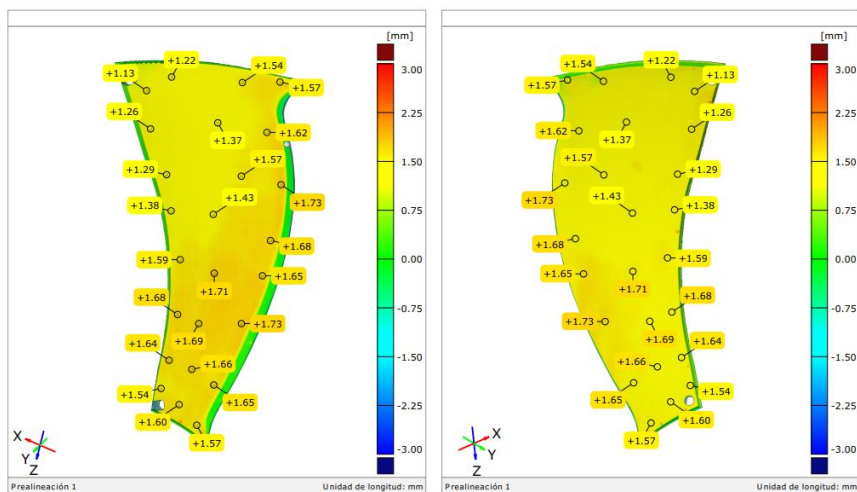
Inspección dimensional computarizada – Inserto #03
